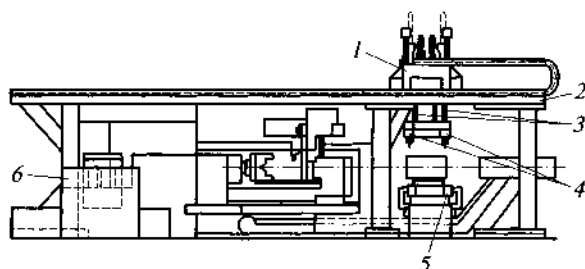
ГПМ на базе токарного станка с фронтальным расположением рабочего органа робота:
